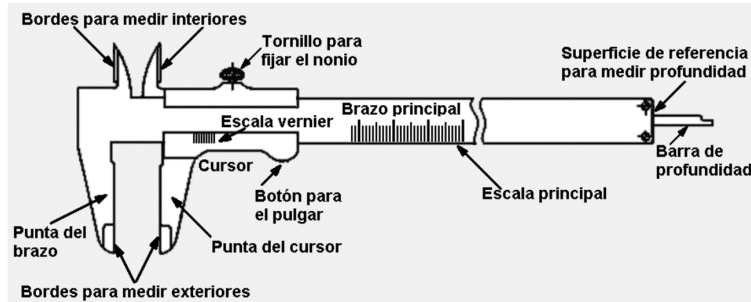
Dibujo esquemático de un calibrador Vernier [2].
